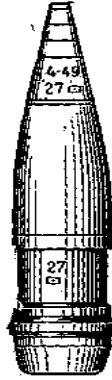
Клейма на снарядах: № партії, рік виготовлення № плавки, проба твердості металу
